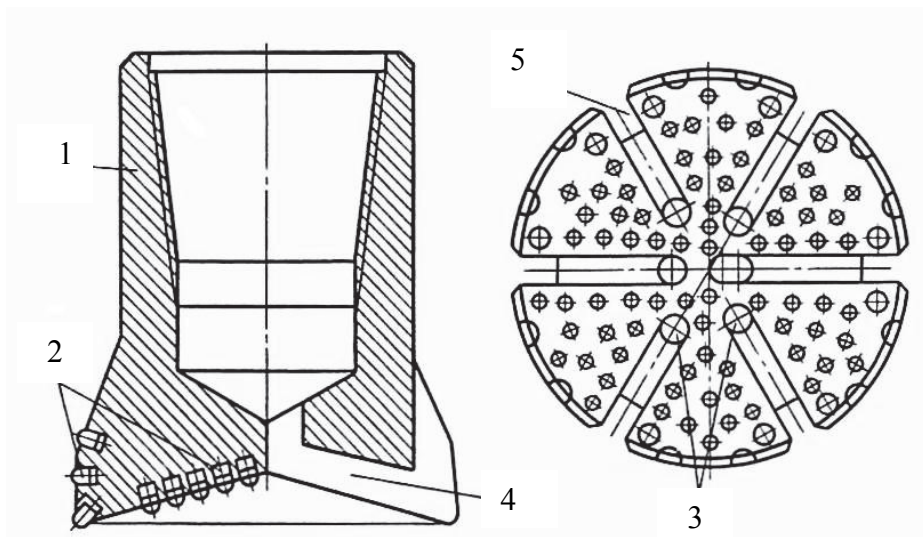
Долото ИСМ с резцами из твердосплавноалмазного композита «Славутич»: 1 – корпус долота; 2 – вставки «Славутич»; 3, 4, 5 – промывочные отверстия и каналы
